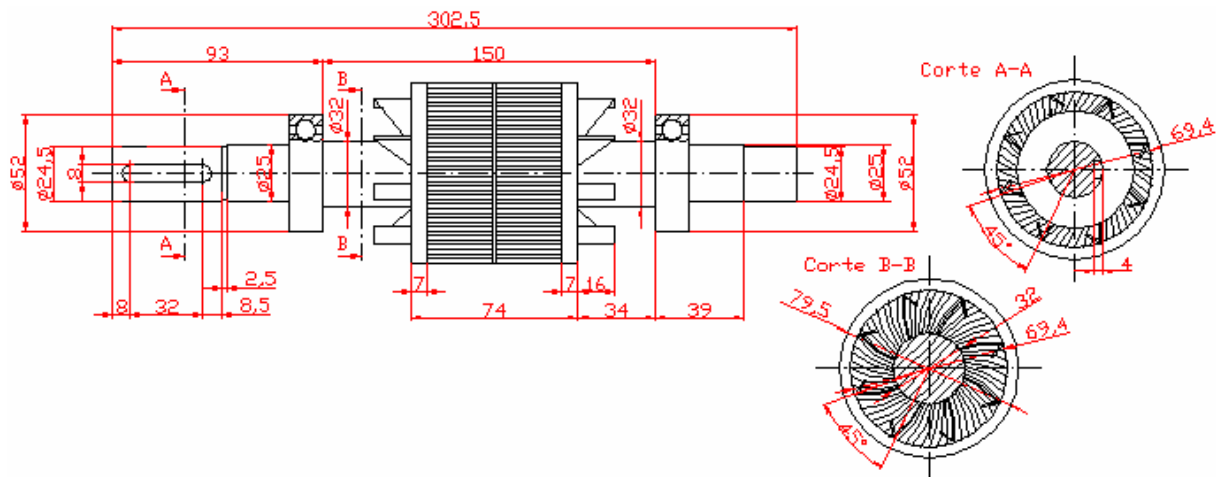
Vista lateral y en planta del rotor de chapas tipo Z. Las cotas están dadas en mm.
